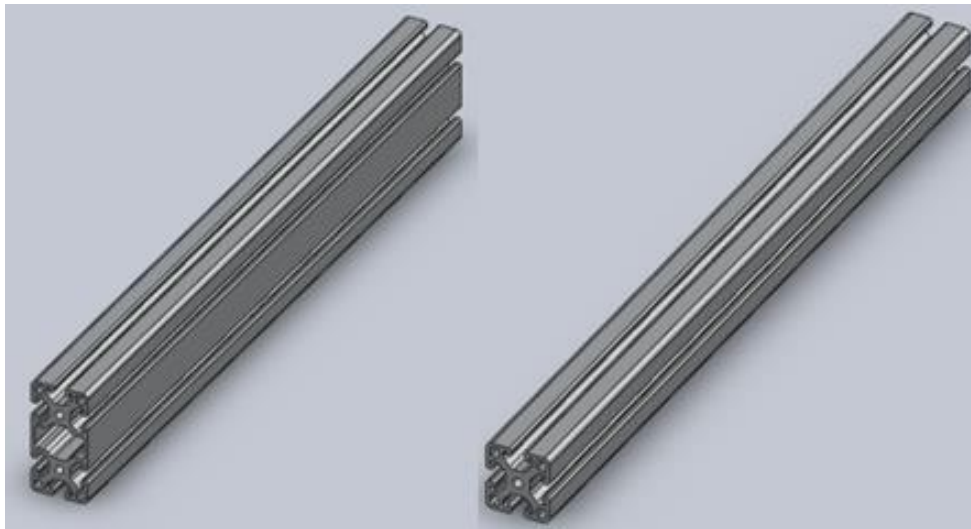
Aluminio estructural 80x40 mm y 40x40 mm
